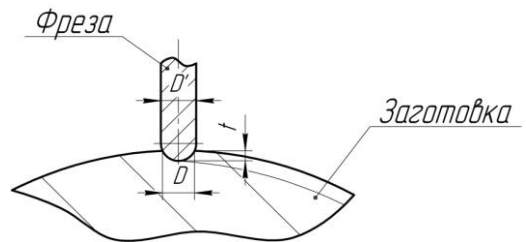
Схема расположения фрезы со сферическим концом относительно заготовки
